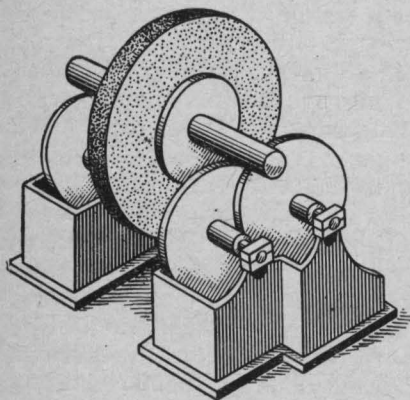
Дисковое приспособление для балансировки абразивных кругов.
